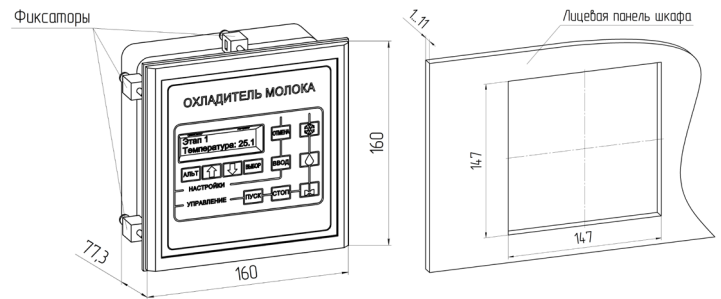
эскиз контроллера и монтажного отверстия.
